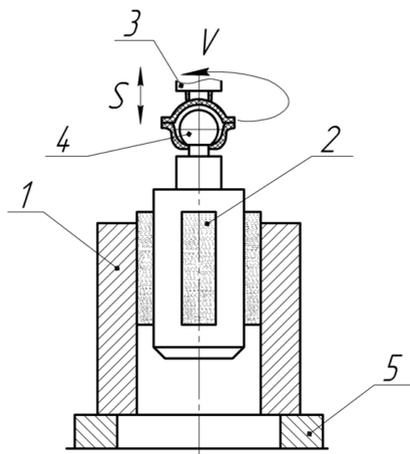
Схема хонингования внутренних поверхностей цилиндрических деталей: 1 — обрабатываемая деталь; 2 — хонинговальная головка; 3 — шпиндель; 4 — шарнир; 5 — станина
